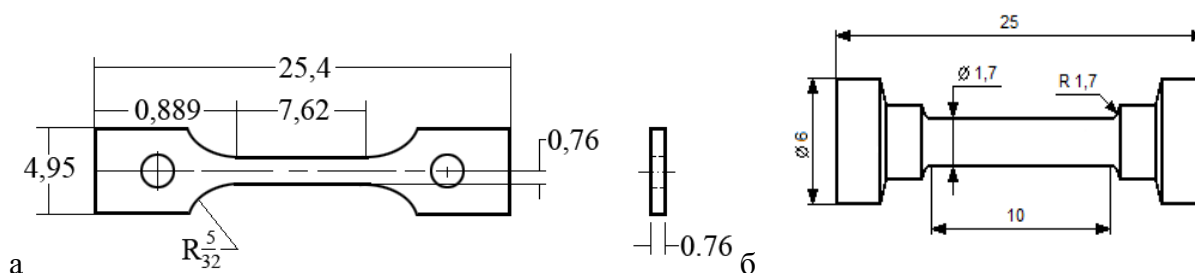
Форма и габаритные размеры образца формата SS-3 (а) и цилиндрического образца для растяжения (б).
